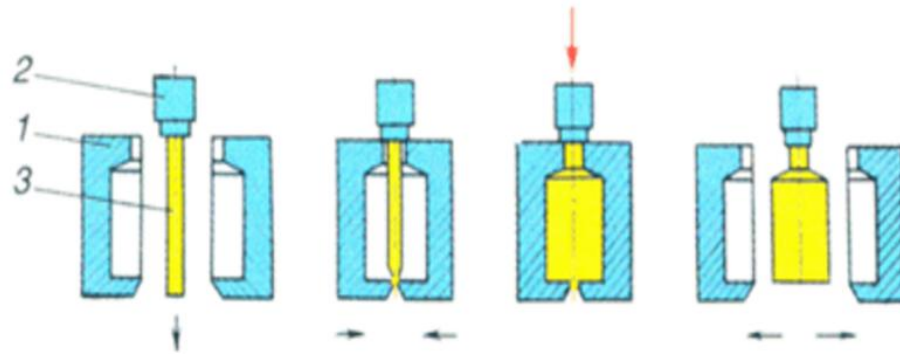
Схема екструзійно-видувного формування для виготовлення пляшок
